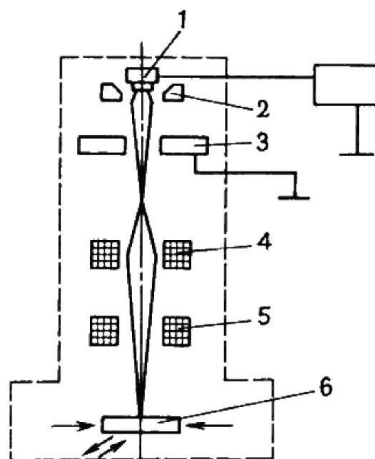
Схема установки для электронно-дуговой сварки
